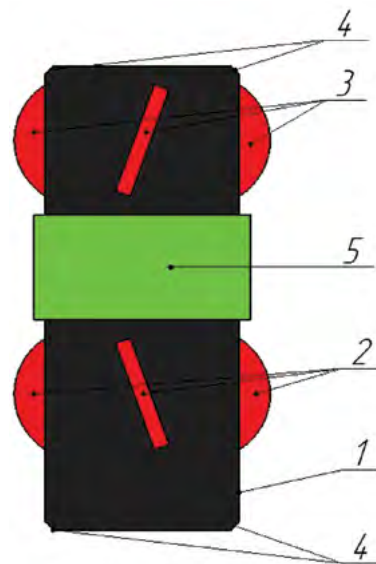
Принципиальная схема центратора-смесителя для эксплуатационной колонны из полимерных труб: 1 — корпус центратора-смесителя; 2 — лопасти нижнего яруса; 3 — лопасти верхнего яруса; 4 — фаски на торцевой поверхности корпус; 5 — маркер
